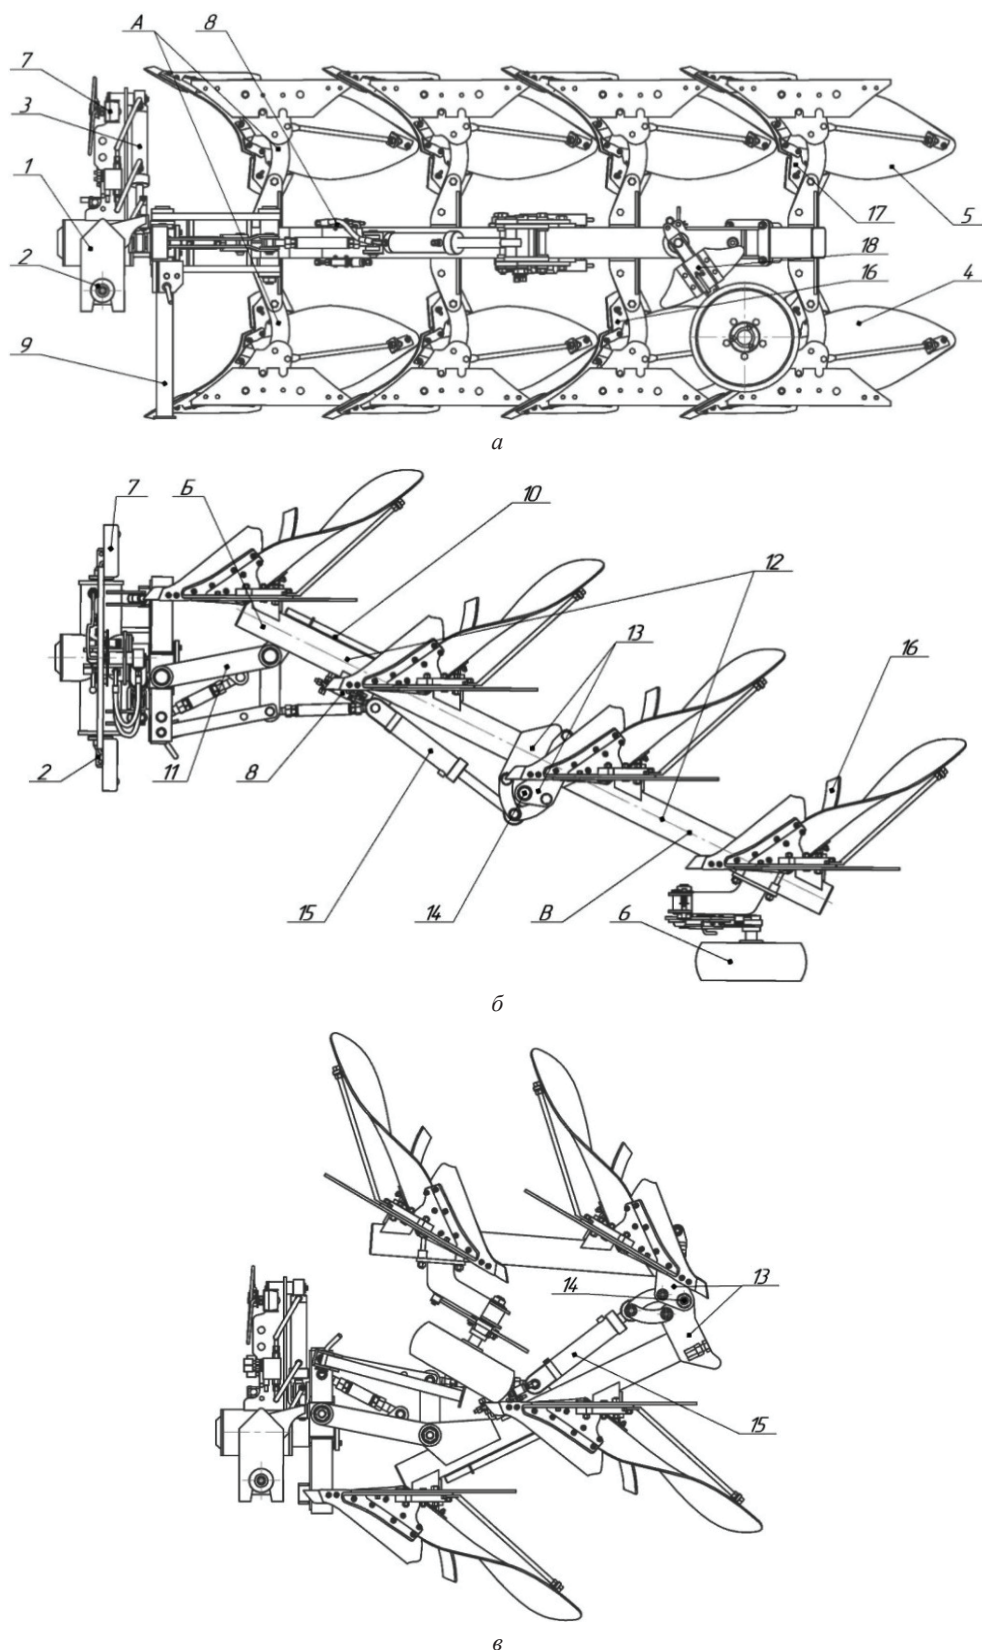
Плуг навесной оборотный со складной рамой: *а* – вид сбоку; *б* – вид сверху; *в* – плуг в транспортном положении; 1 – навесное устройство; 2 – автосцепка; 3 – механизм оборота; 4 – правооборачивающие корпуса; 5 – левооборачивающие корпуса; 6 – колесо опорное; 7 – электрооборудование; 8 – гидросистема; 9 – опора; 10 – чистик; 11 – параллелограммный механизм корректировки ширины захвата; 12 – рама; 13 – кронштейн; 14 – ось; 15 – гидроцилиндр складывания-раскладывания; 16, 17 – углоснимы; 18 – механизм регулировки
